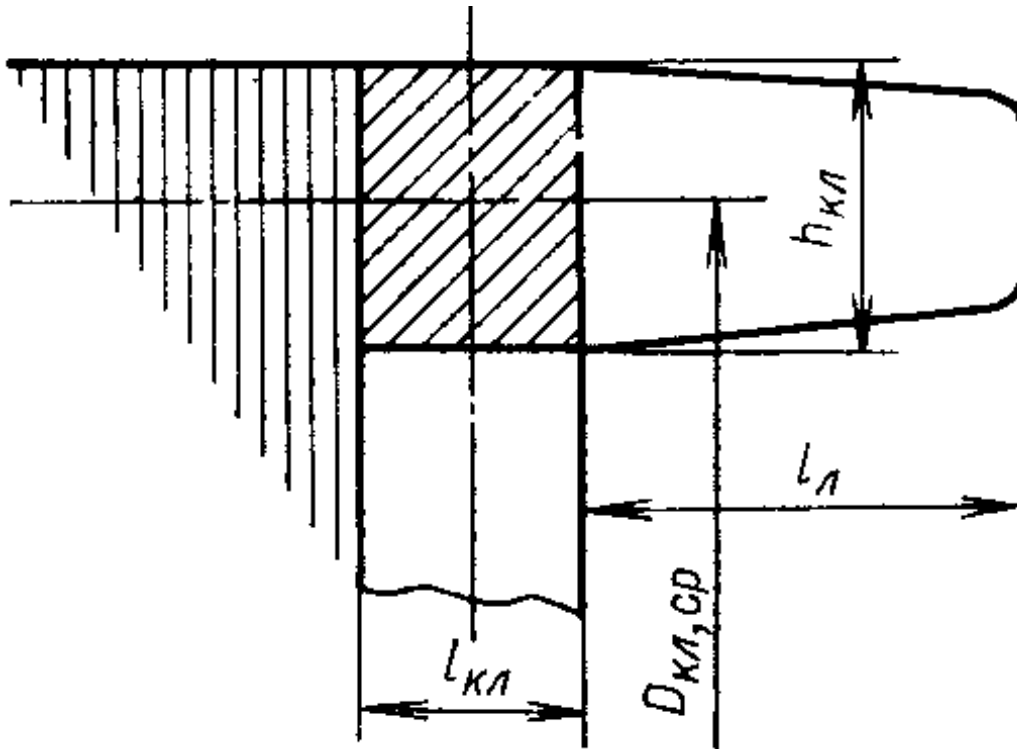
Размеры короткозамыкающего кольца «белочьи клетки» ротора, изготовленной путем заливки алюминия
